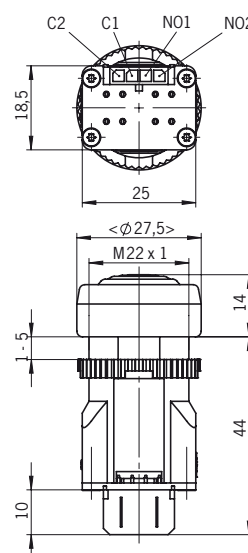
Размерный чертёж выключателя подтверждения ZXE
